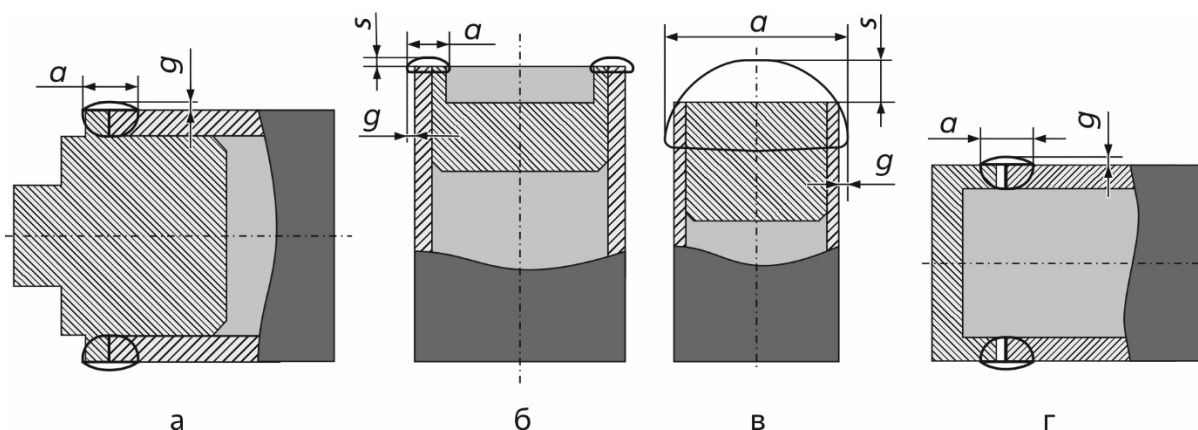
Типовые конструкции сварных соединений экспериментальных образцов: торцовая точечная (а), торцовая кольцевая (б), кольцевая стыкозамковая (в) и стыковая (г): a – ширина сварного шва; g – усиление сварного шва; s – увеличение высоты шва после сварки
